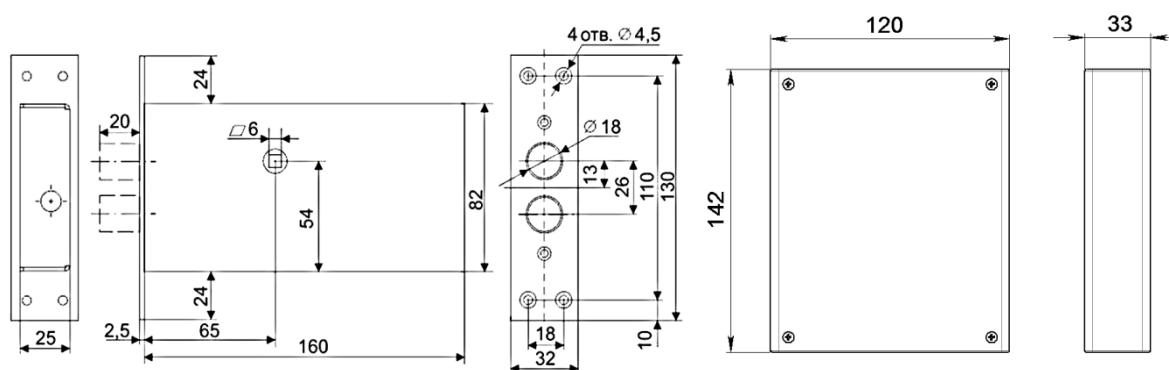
Габаритно-присоединительные размеры корпуса ЭМЗ 1.2 и блока управления GSM.
